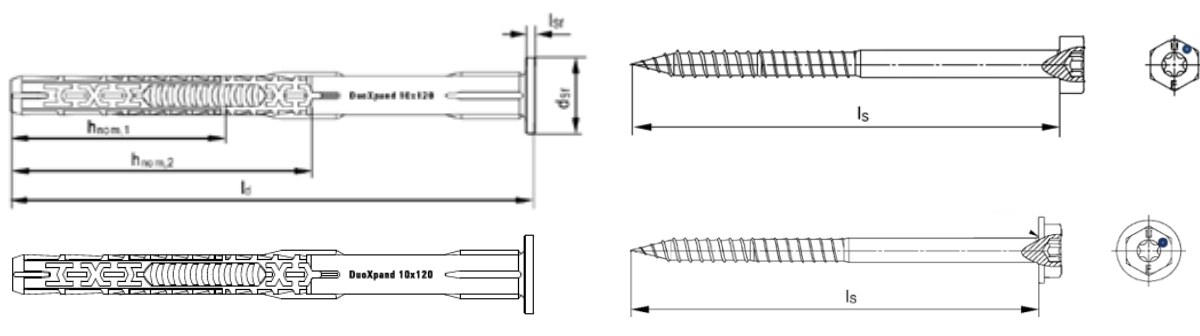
Technische Zeichnungen der Dübelhülse und Sechskantschraube (s. rechts oben) und Sechskantschraube mit angepresster Unterlegscheibe (s. rechts unten)
